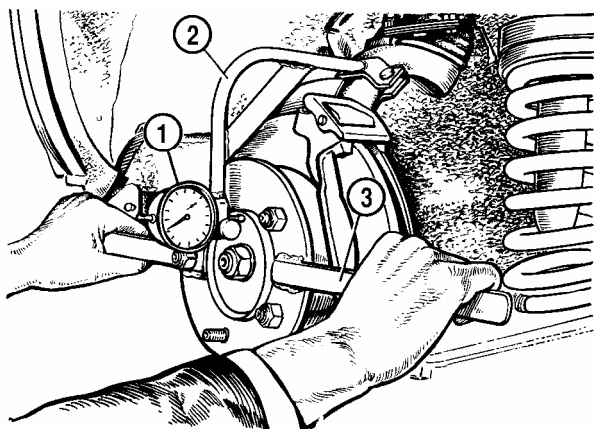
Проверка осевого зазора в подшипниках ступицы переднего колеса:
